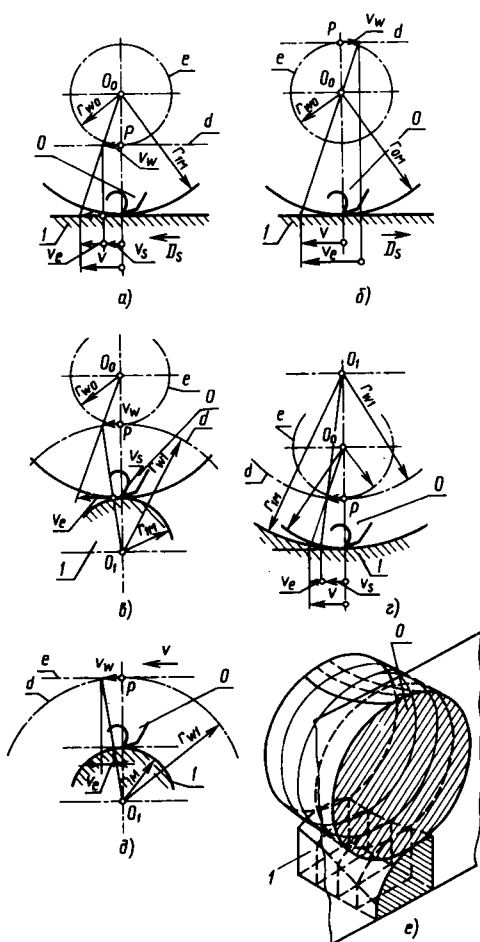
Схема работы обкатного инструмента с компланарными векторами скоростей главного и обкатного движений
